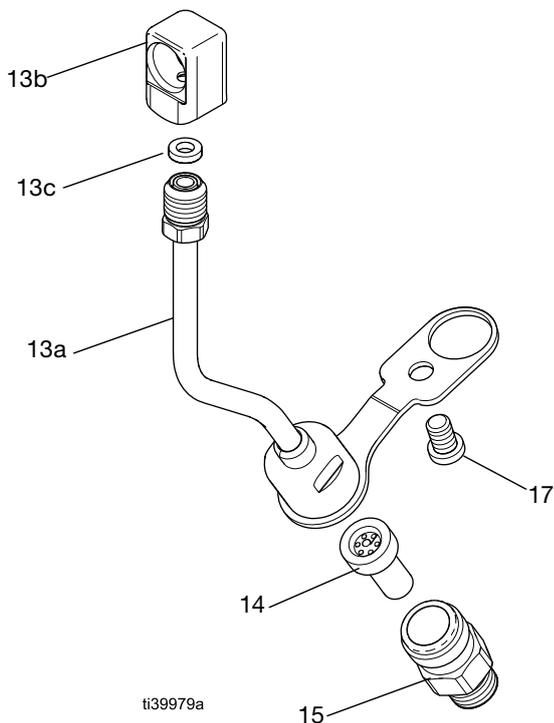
Ensemble de tuyau de fluide : modèle 26B711
